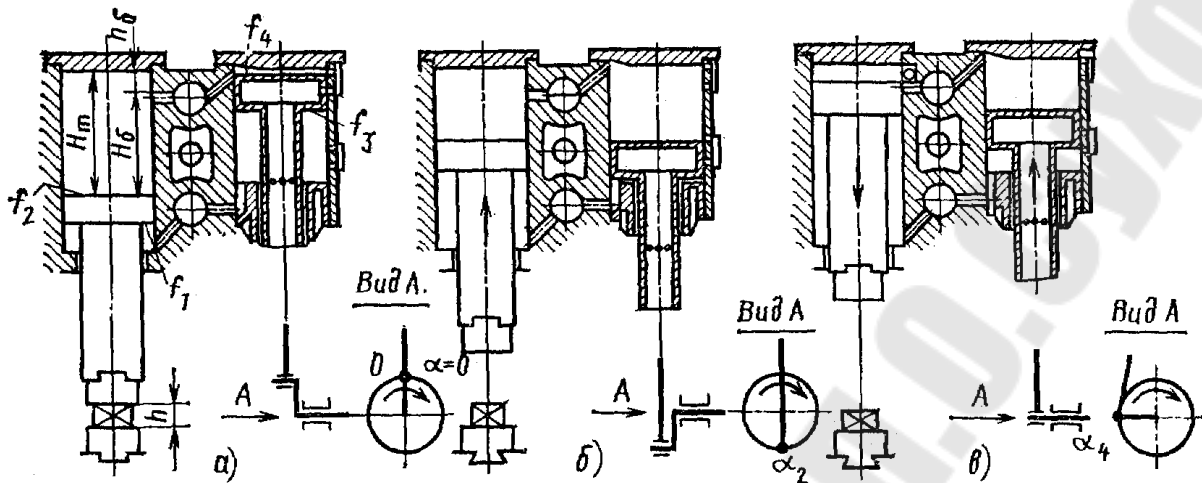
Схема движения поршней рабочего и компрессорного цилиндров:
